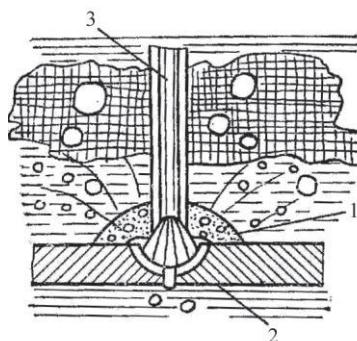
Сварка под водой: 1 – газовый пузырь окружающий дугу; 2 – изделие; 3 – электрод
